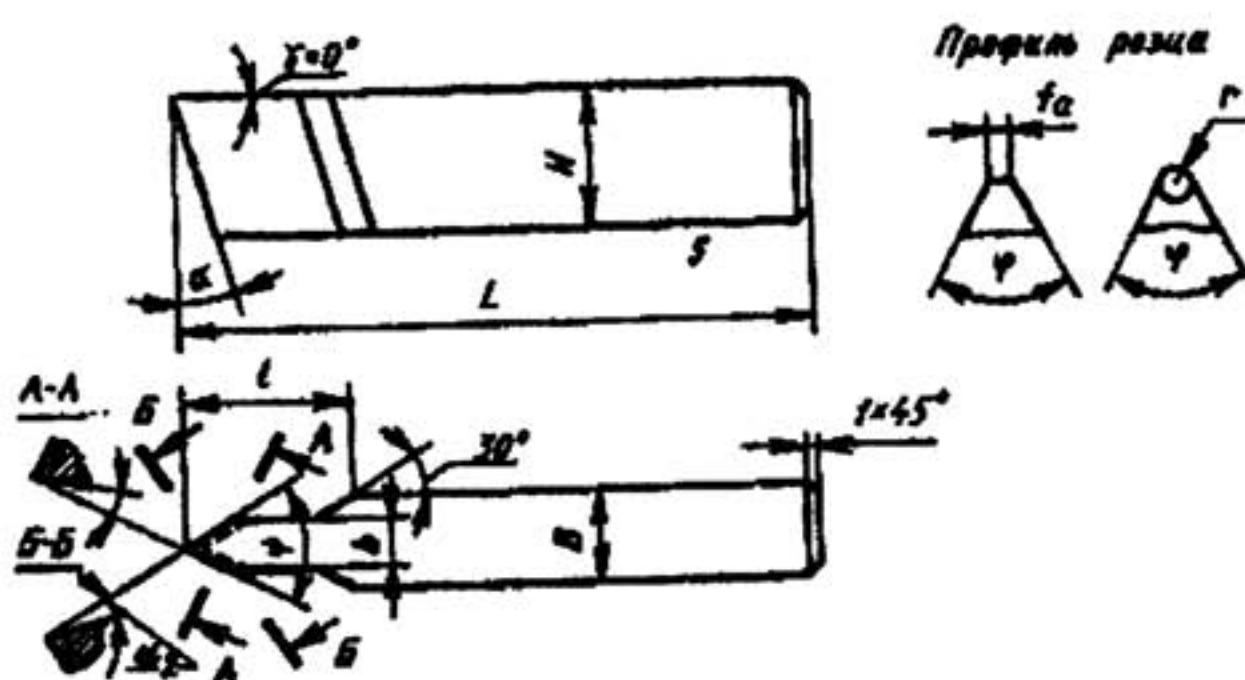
Стержневой резьбовой резец из быстрорежущей стали
